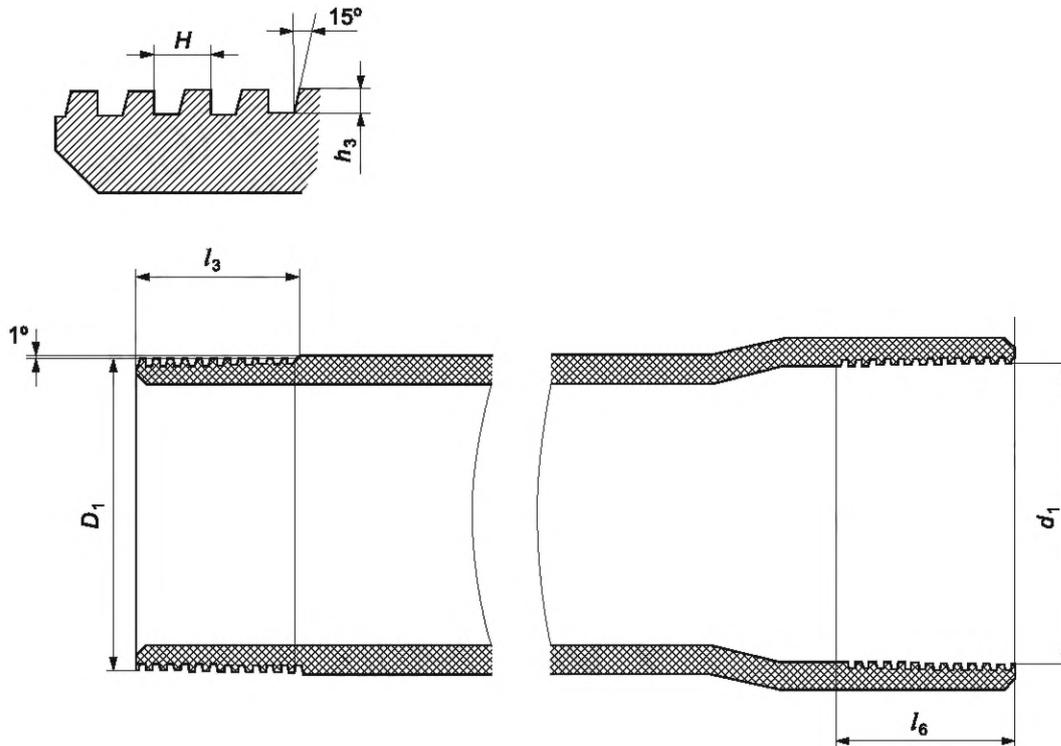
Размеры и профиль упорной конической резьбы
